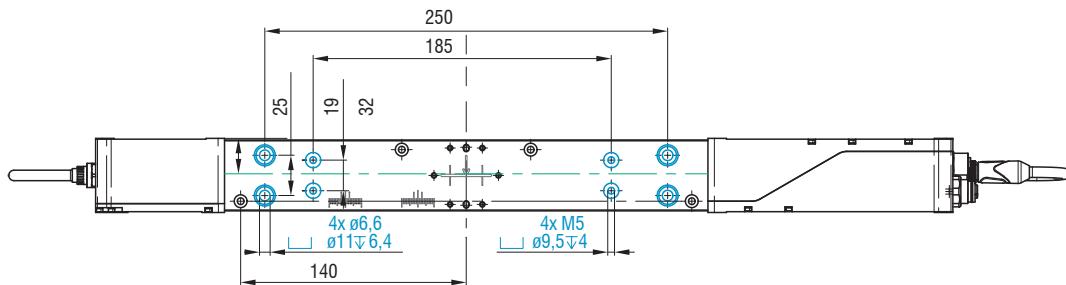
Maßzeichnung Montageschiene ODC2700-10, ODC2700-40, optionale Montage
